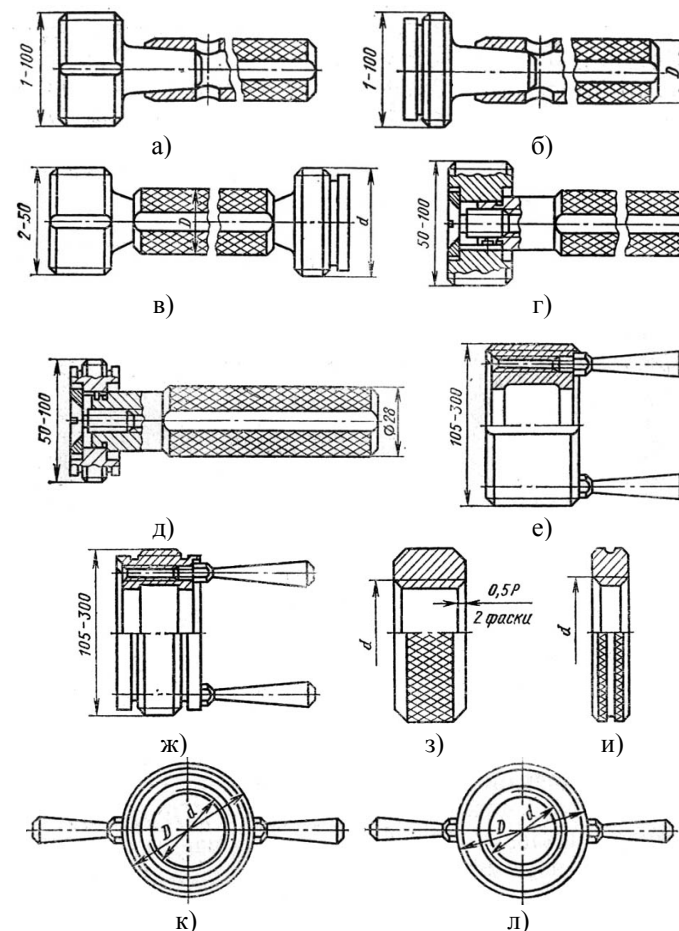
Конструкция резьбовых калибров-пробок и калибров колец: а), б), в) – со вставками; г), д) – с насадкой; е), ж) – с ручками; з) и) – без ручек; к), л) – с ручками на боковой поверхности
